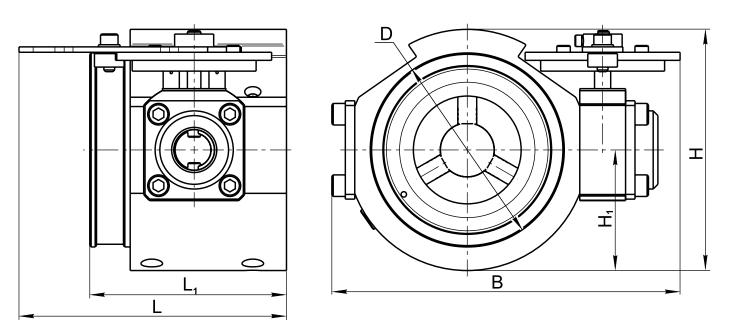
Габаритные и присоединительные размеры для смесителей типа СГ...-Р
